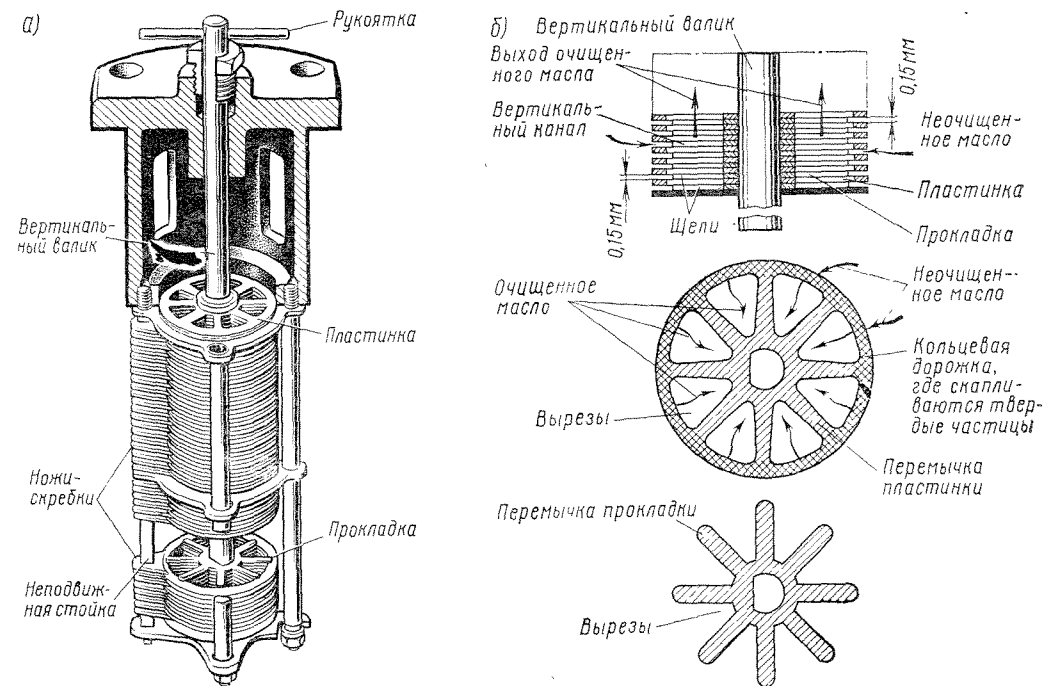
Устройство пластинчато-щелевого фильтра грубой очистки масла
